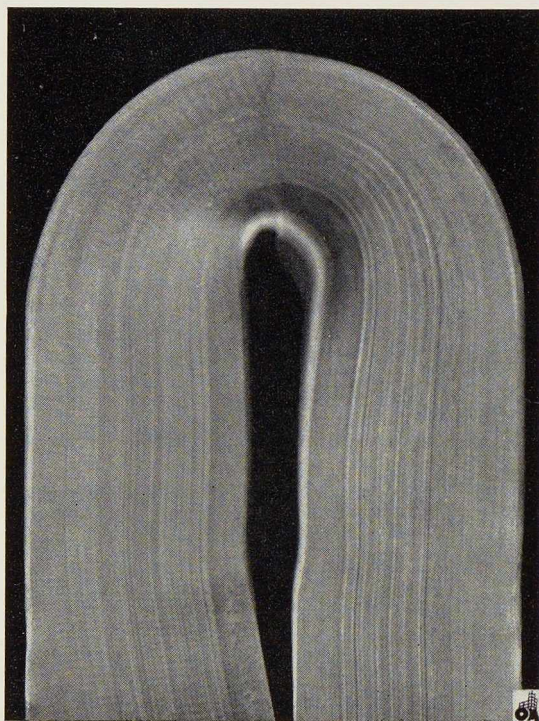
Macrographie d'une éprouvette soudée après pliage.
